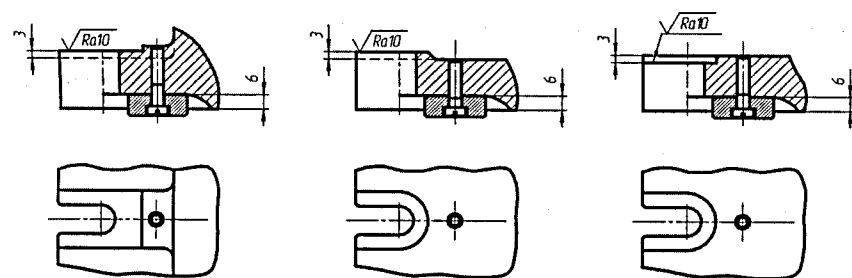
Конструкції провувшин у корпусах приспосувань
